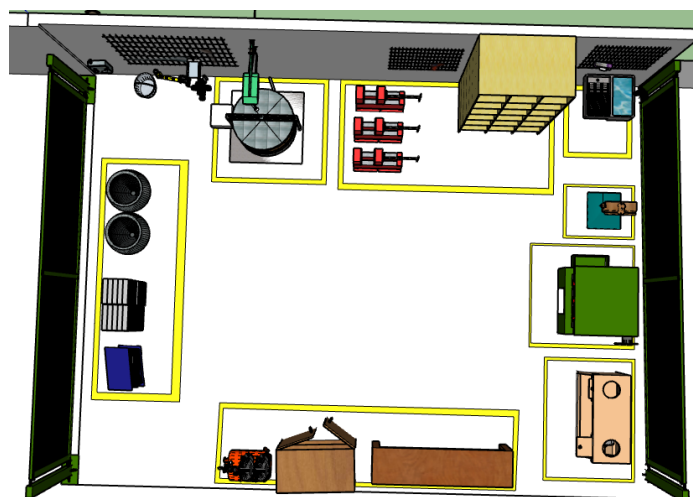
Propuesta Diseño de Planta Vista Superior. Fuente: Elaboración Propia
